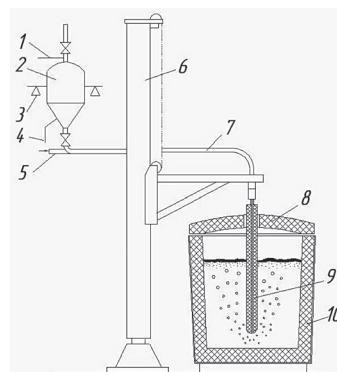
Устройство для продувки стали кальцийсодержащими реагентами: 1 – линия наддува; 2 – раздаточный бункер; 3 – весоизмерительное устройство; 4 – линия создания псевдоожижения; 5 – транспортная линия; 6 – стойка; 7 – линия подачи материала; 8 – крышка; 9 – фурма; 10 – ковш
